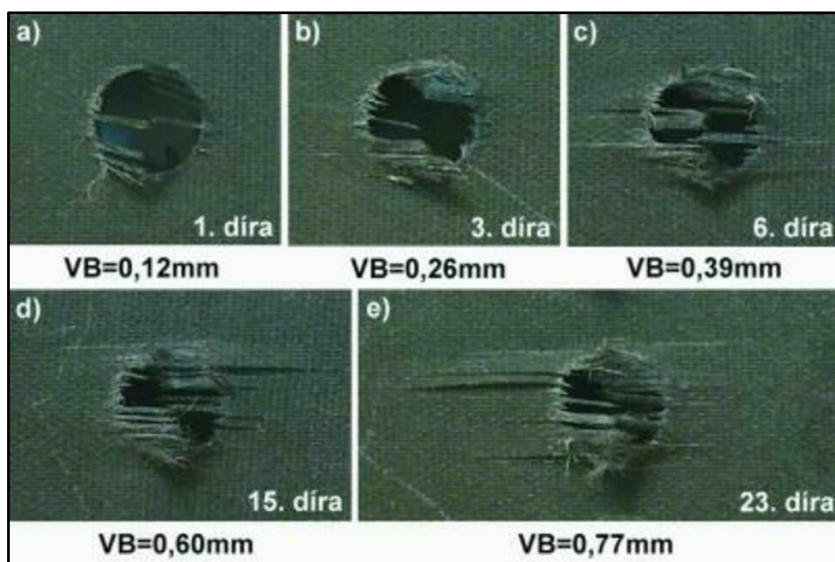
Princip vzniku delaminace při vrtání [16]
